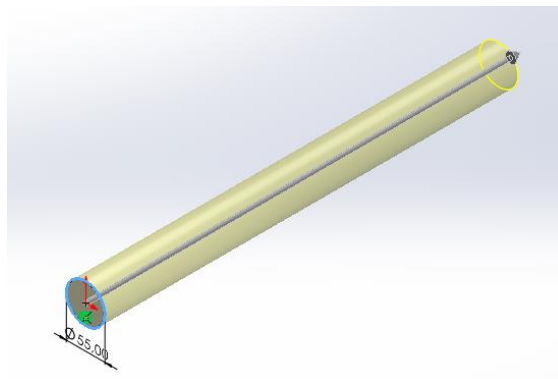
Extrusión eje de la herramienta en SolidWorks.
